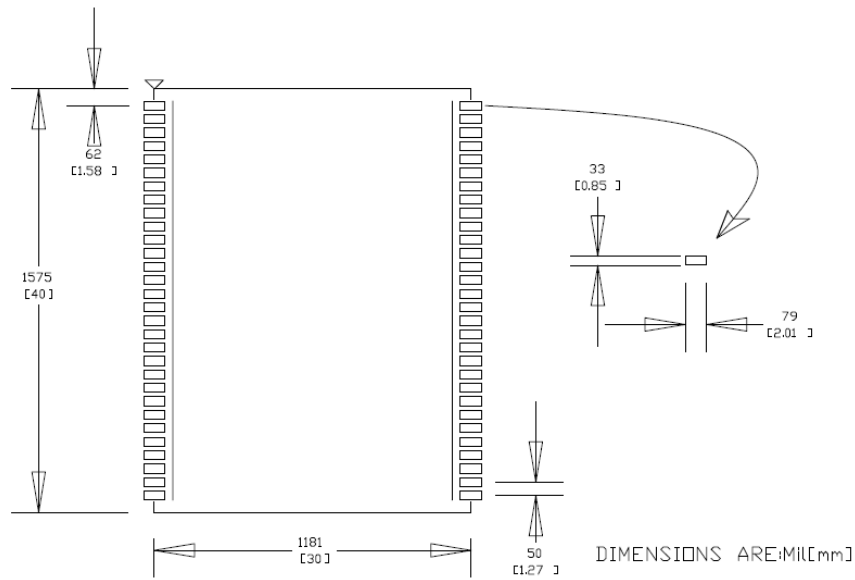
推荐 PCB 封装设计 (尺寸单位: mil, 括号内单位: mm)
